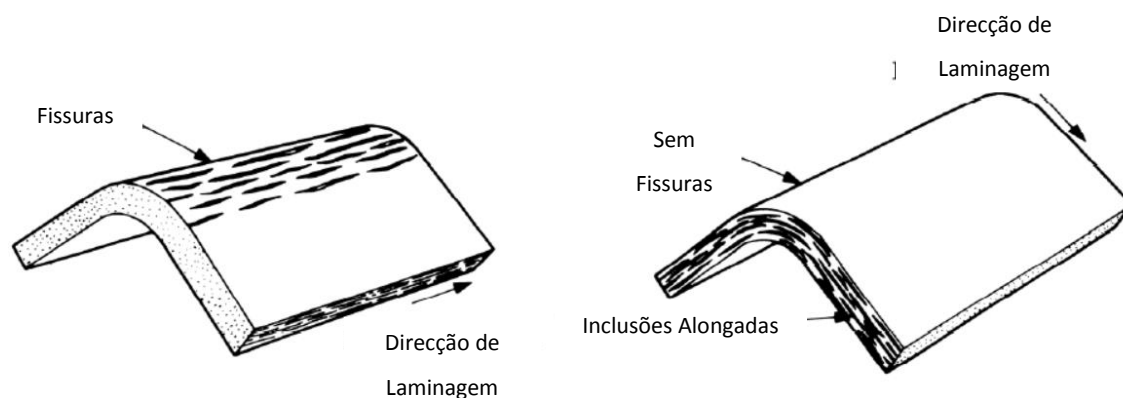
Direcção de laminagem e fissuras que podem acontecer na quinagem (Francisco Silva, 2007)
